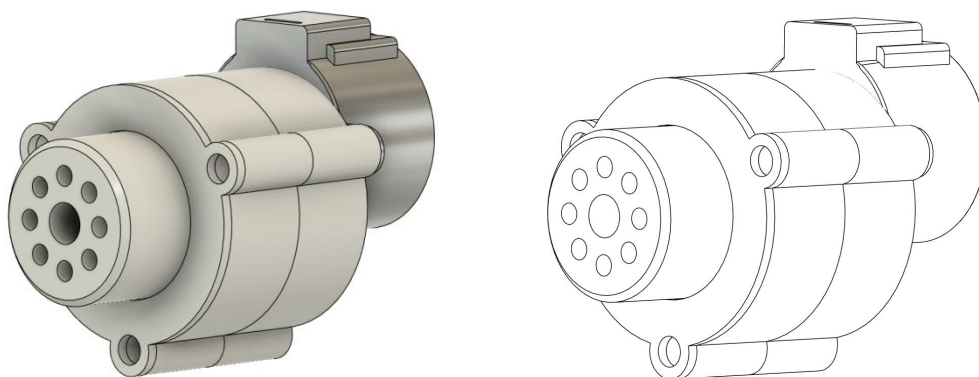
Зібраний планетарний редуктор 16:1
